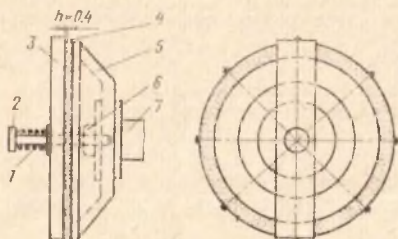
Схема установки базовых пластин и съемной планки на алмазный круг:
